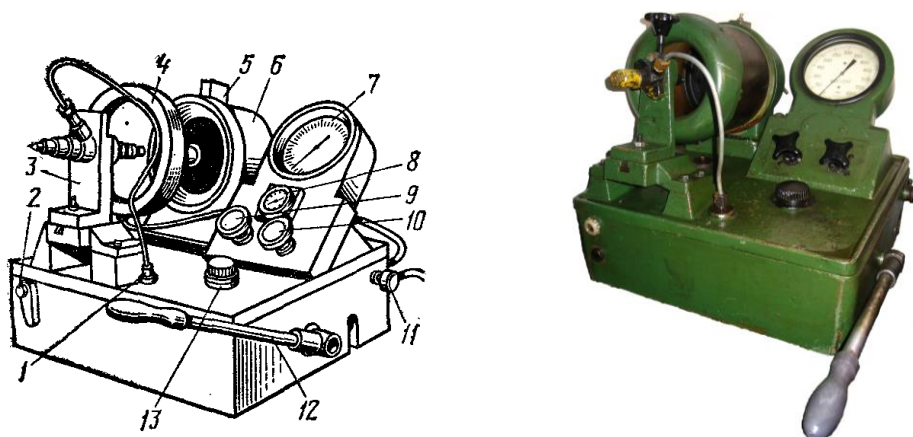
Прилад КИ-562 (КИ-1609А) для випробовування і регулювання форсунок:
